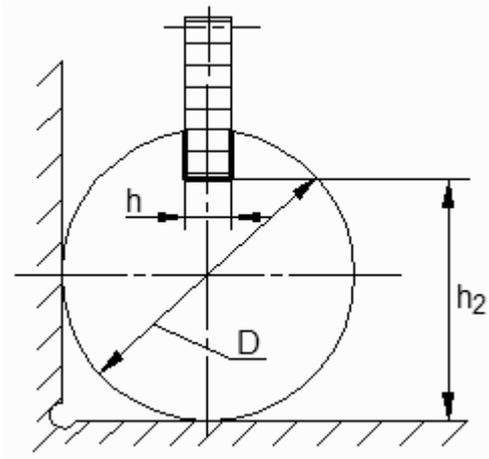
Схема фрезерования шпоночного паза на валу.
